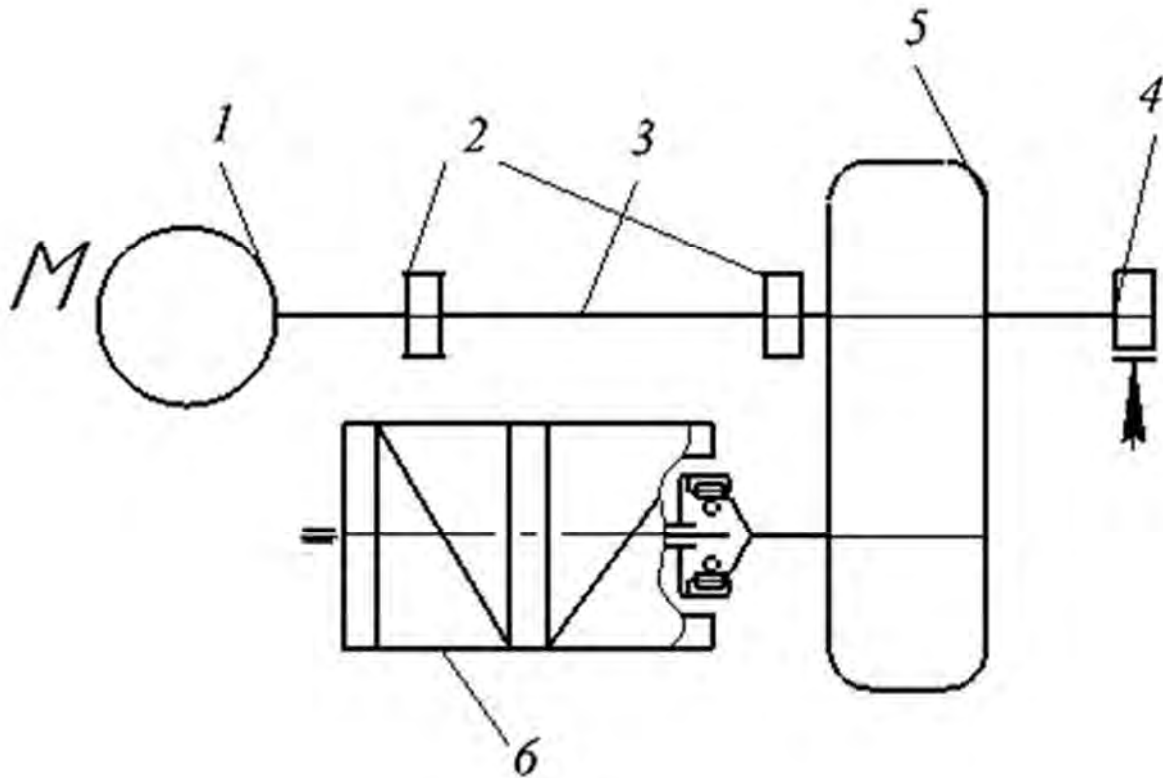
Кинематическая схема механизма подъема: 1 – электродвигатель; 2 – муфта зубчатая; 3 – промежуточный вал; 4 – тормоз; 5 – редуктор; 6 – канатный барабан
